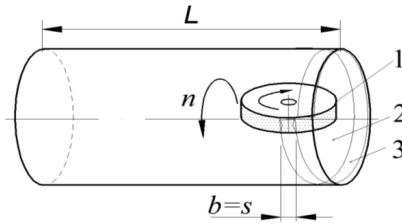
Схема обробки внутрішньої поверхні циліндра:
